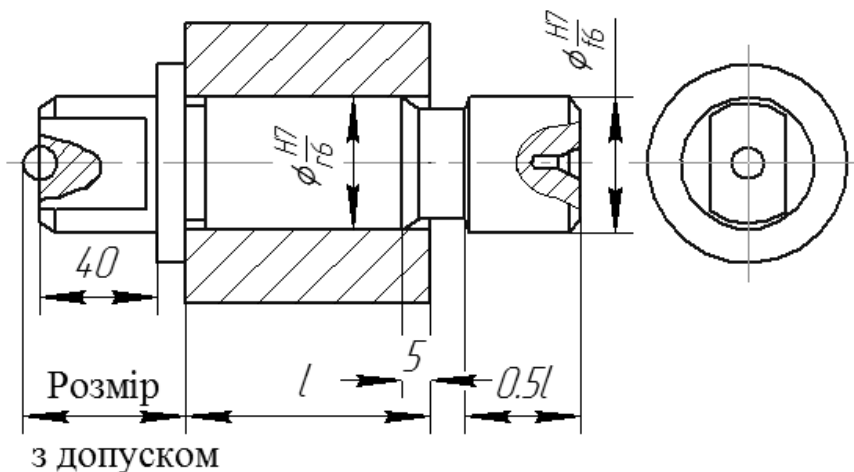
Установка заготовок на жорсткій оправці (посадка з натягом)
